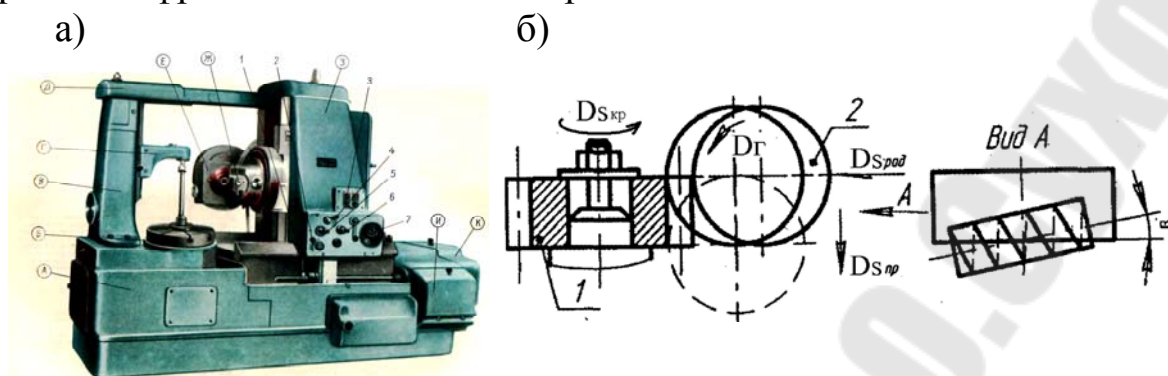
Общий вид зубофрезерного станка (а) и схема обработки зубчатого колес (б)
